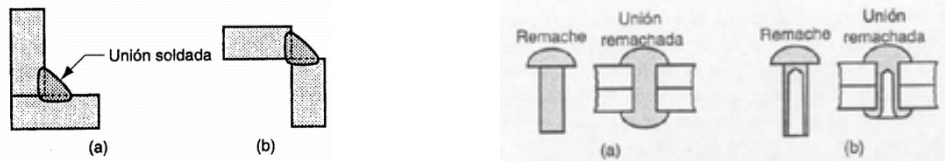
, Ensamble por medio de Soldadura o Remache, Fuente: (Juan, 2013).
